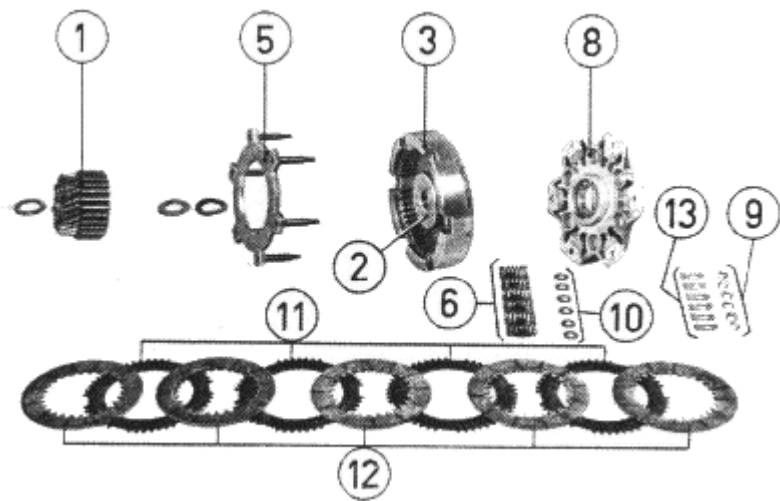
Kupplung zerlegt (verschweißte Ausführung)
